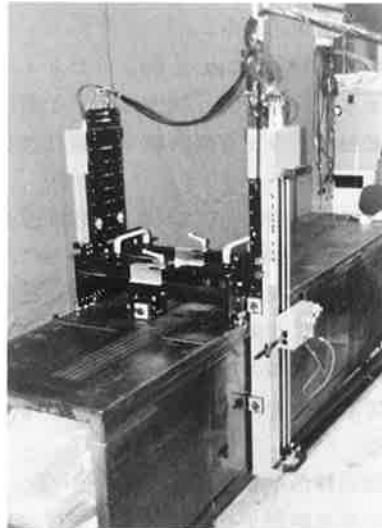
ダイヤフラムエレクトロスラグ溶接部自動探傷装置
